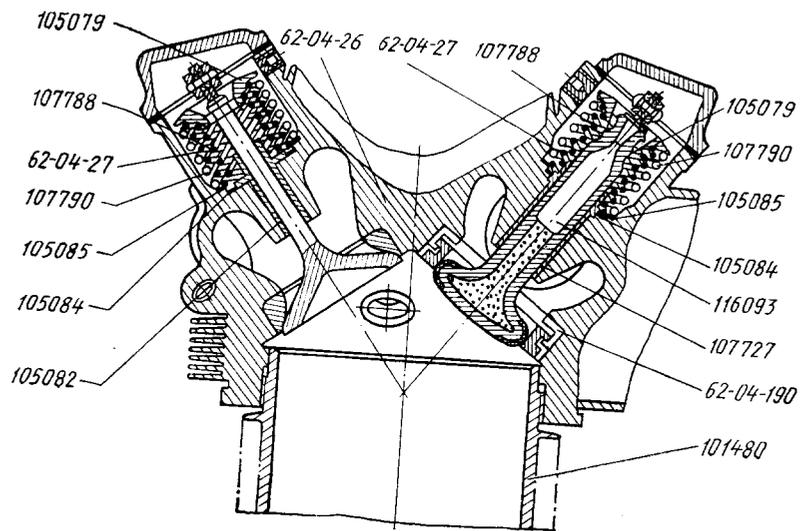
Цилиндр (в сборе) 62-04-180 двигателей
